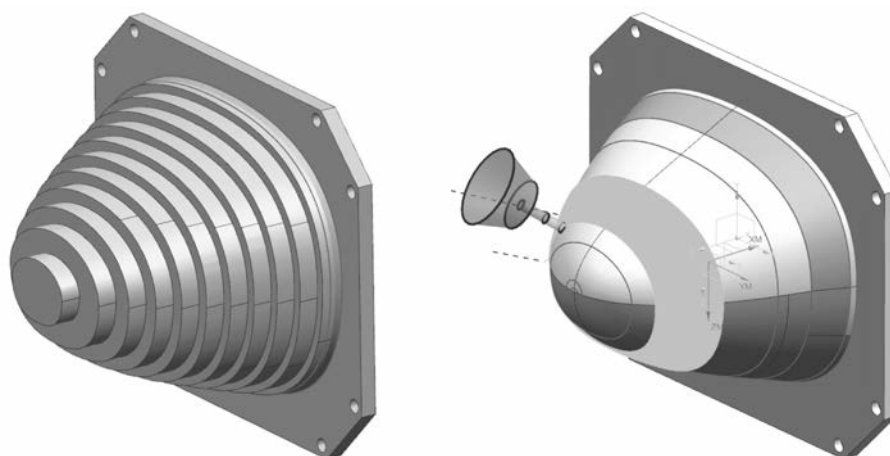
Заготовка носового кока вертолётного производства и процесс обработки в системе UG/NX
